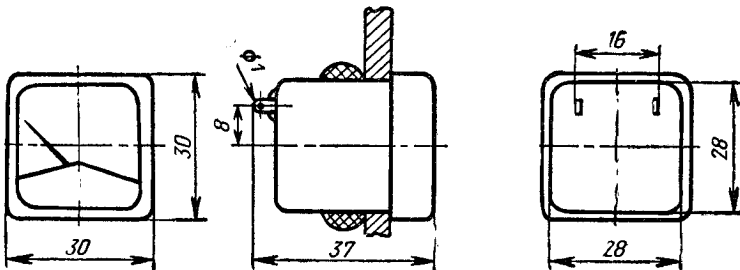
Габаритный чертеж прибора типа М4223.
